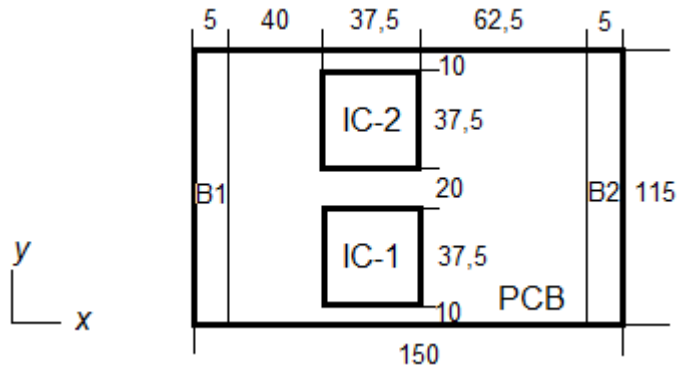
Esquema de la geometría de la tarjeta (vista en planta por arriba; cotas en mm).
